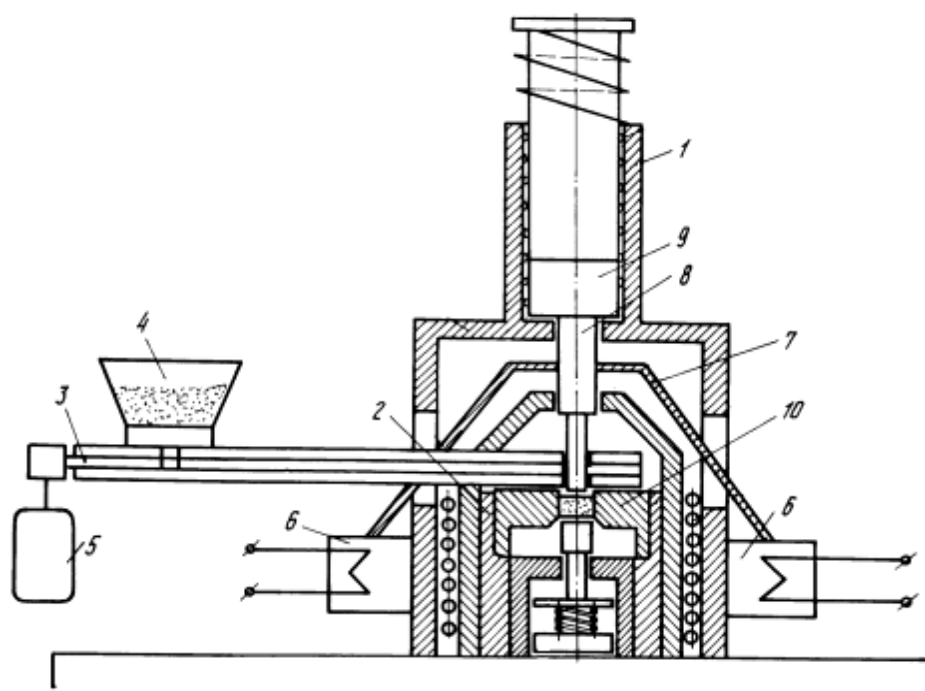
Установка для ударного уплотнения таблеток ядерного топлива [8], автор Горишний В. А.: 1 – электрический молот; 2 – пресс-штамп; 3 – роторный магазин; 4 – загрузочный бункер; 5 – электропривод; 6 – электромагниты; 7 – коромысло; 8 – верхний пуасон; 9 – боек; 10 – матрица
